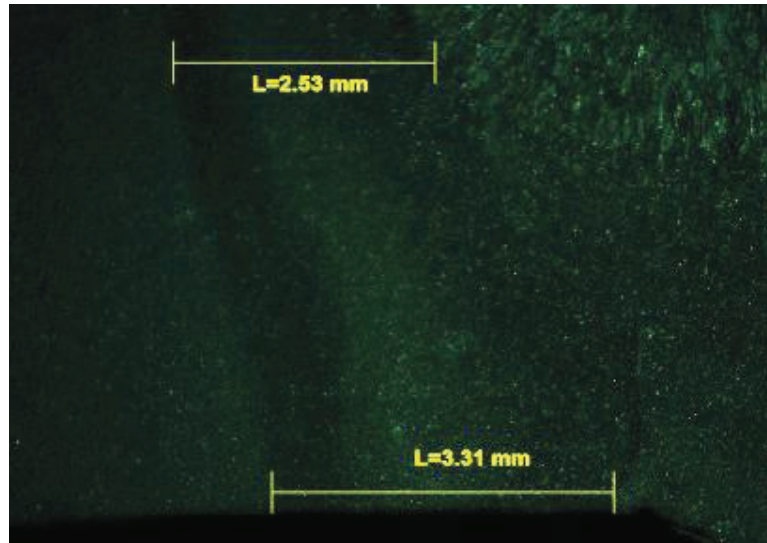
8 Macrografía del primer pase (raíz) de soldadura realizado con proceso SMAW (6G), presenta buena penetración y fusión, 30X. Las dimensiones indican la longitud de la zona de soldadura y las zonas afectadas por el calor.
